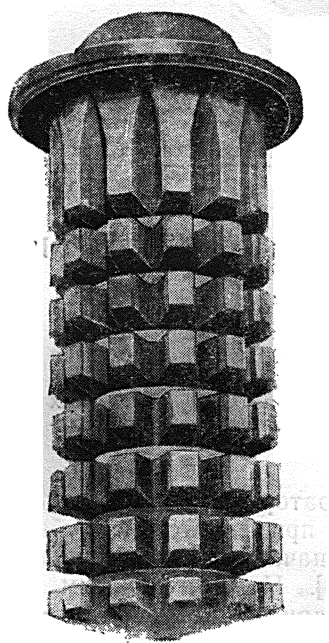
Вapотронный коллектор с зубчатым оребрением.
